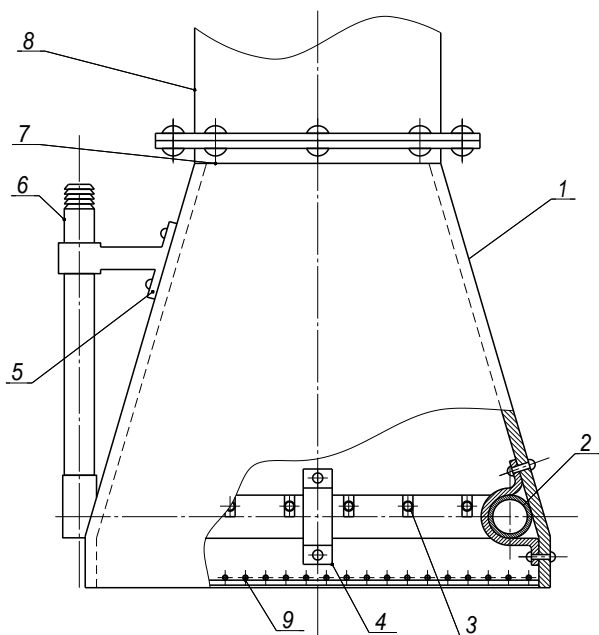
Пневматичний забірний пристрій: 1 - корпус; 2 - кільцевий напірний трубопровід; 3 - форсунки; 4, 5 - кронштейни; 6 - магістраль подачі повітря; 7- вихідне вікно; 8 - транспортуючий трубопровід; 9 - захисна решітка
